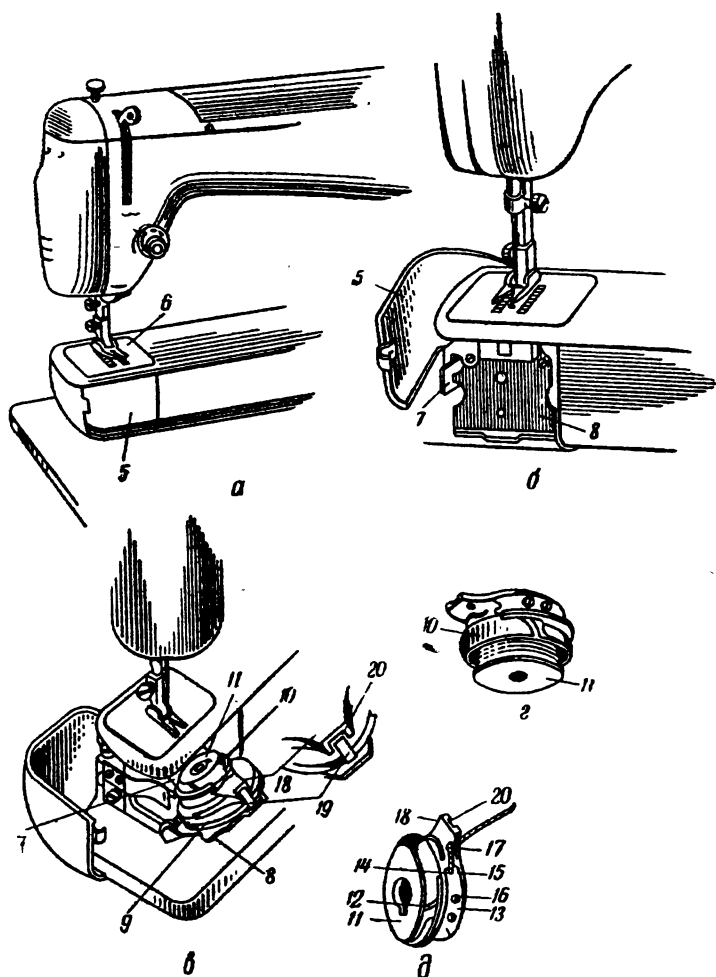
Выемка и вставка шпуледержателя в машине «Лада» Т-132-2 кл.: а — челночный комплект, закрытый боковой крышечкой; б — пружина для открытия стойки держателя; в — открытая (откинутая) стойка держателя; г — освобождение шпульки из шпуледержателя; д — заправка нижней нитки (нити от шпульки) в шпуледержателе
